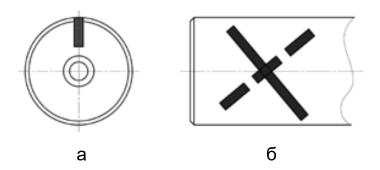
Примеры нанесения меток на торцевую (а) и боковую (б) поверхности свободного конца вала.
